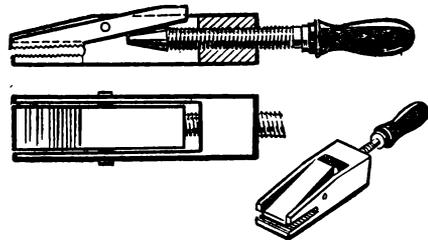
Приспособление для зажима мелких деталей при сверлении в них отверстий.
